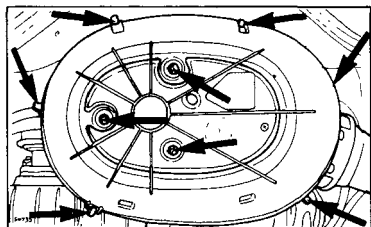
Двигатель OHC — крепежная гайка, винт и зажимы воздушного фильтра (указаны стрелками)
